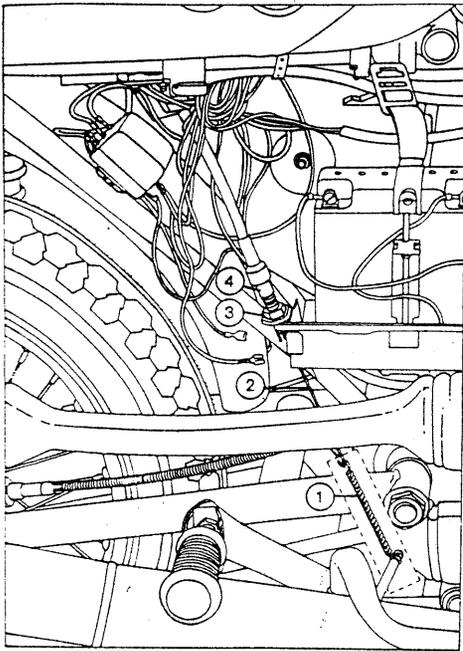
Contacteur de stop – régler la pédale de frein arrière
